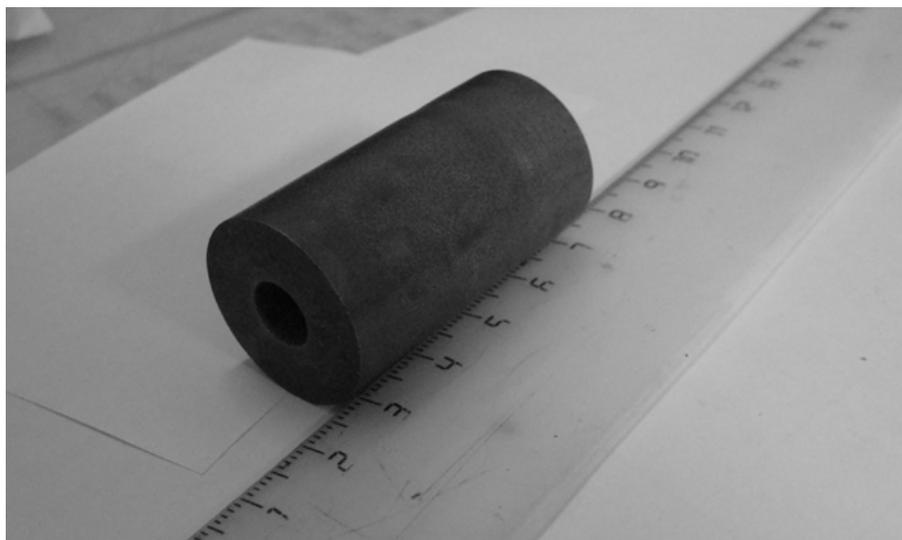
Заготовка из спеченного твердого сплава под мелко модульную червячную фрезу.
